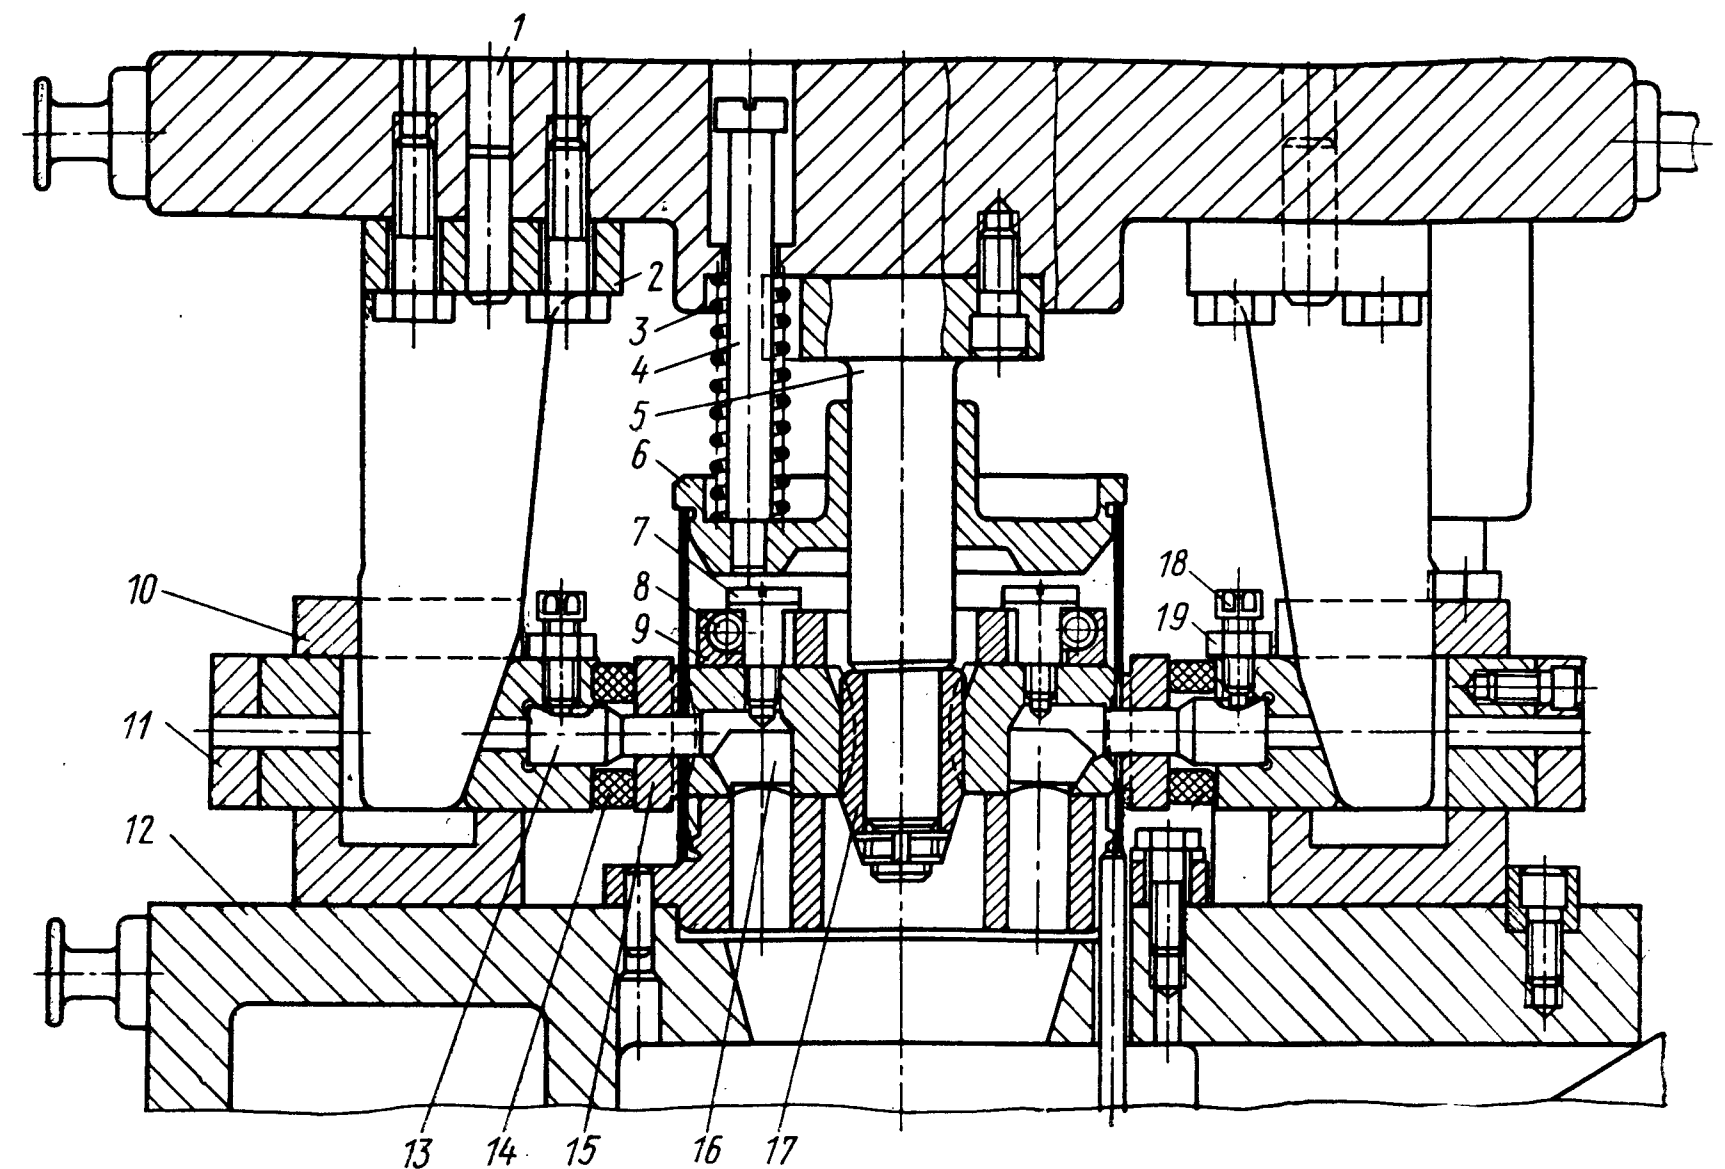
Штамп с раздвижными матрицами для пробивки отверстий в обечайке
